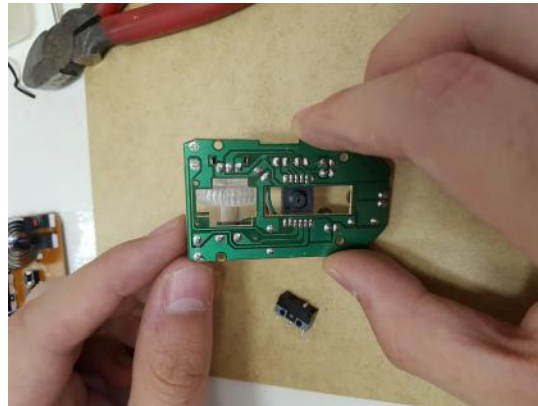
Parte posterior da PCB do mouse com apenas um botão
